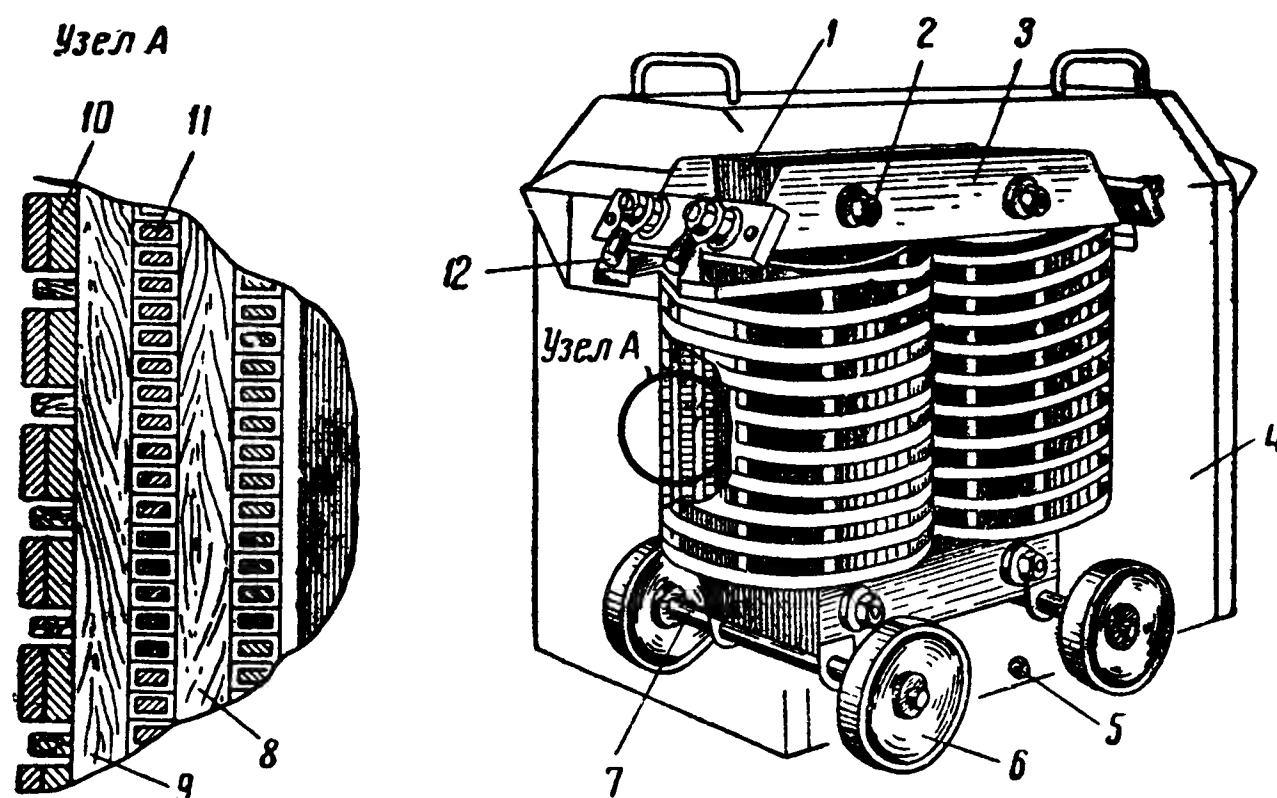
Сварочный трансформатор СТЭ-34-У
